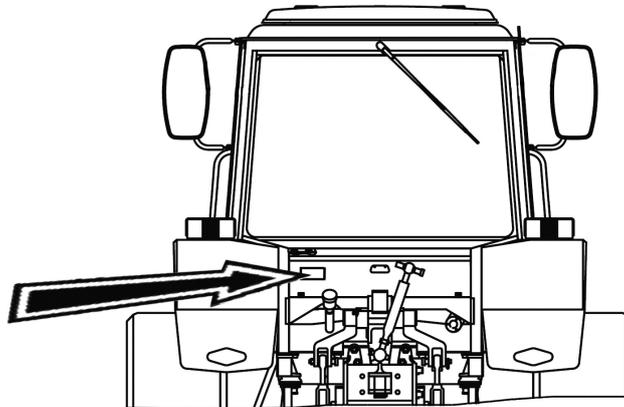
Место расположения фирменной маркировочной таблички трактора
